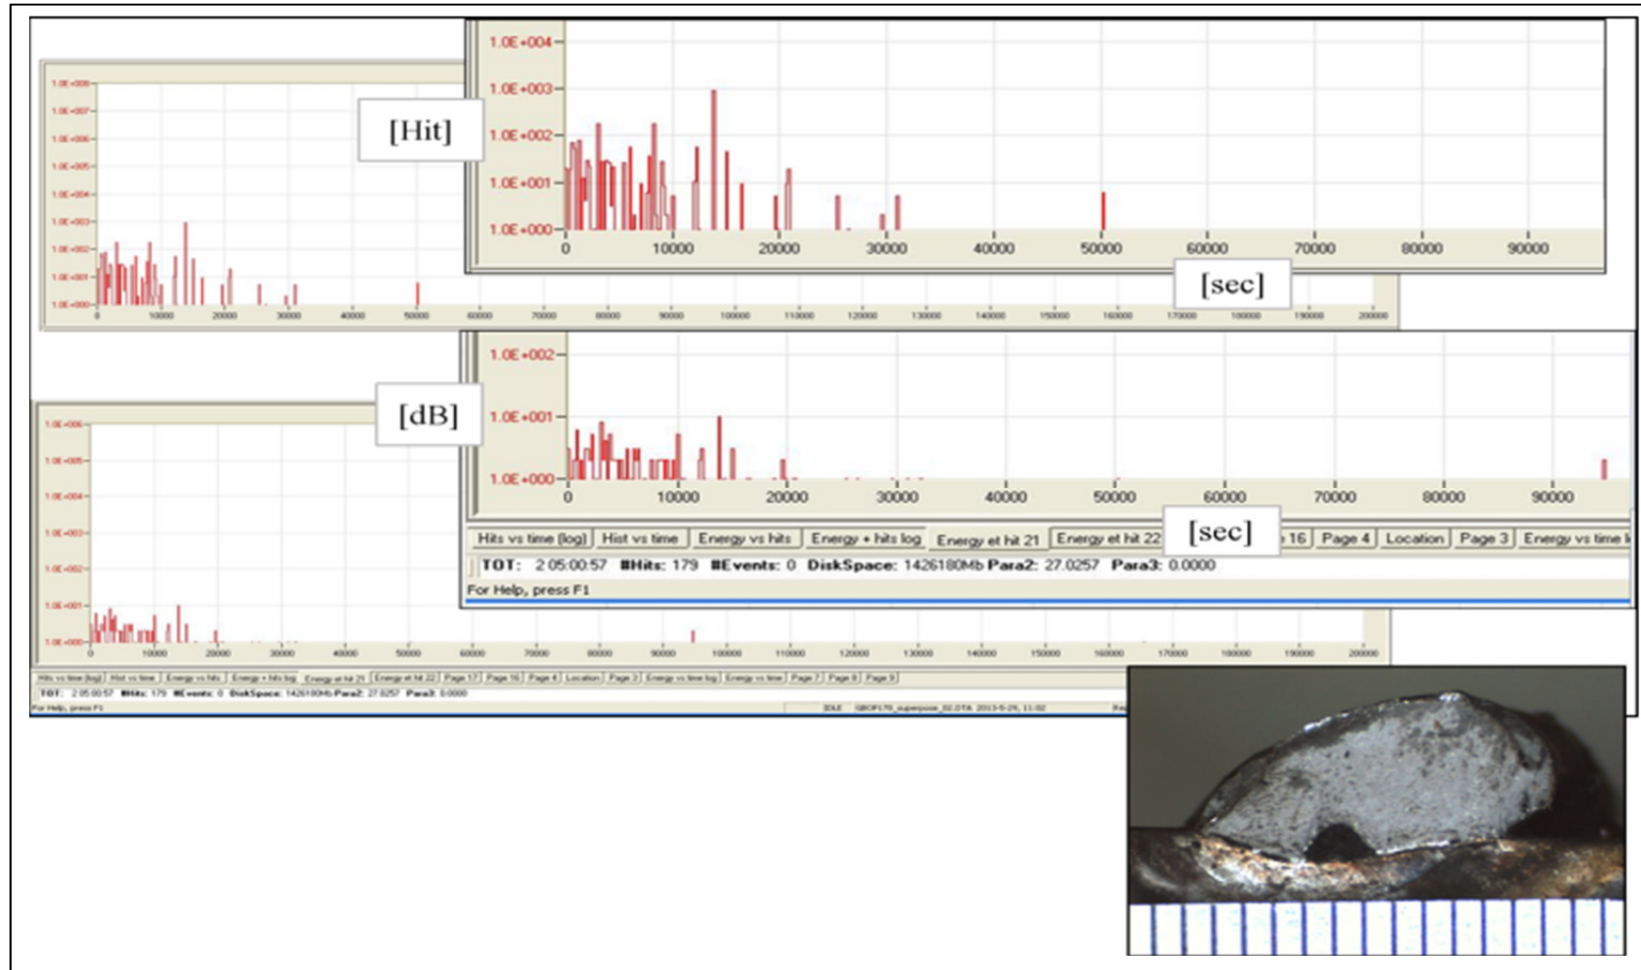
Résultat d'un essai d'émission acoustique sur une éprouvette GBOP et surfaces de rupture de cette même éprouvette. Soudure faite avec préchauffage à 178°C et sans montage de refroidissement
